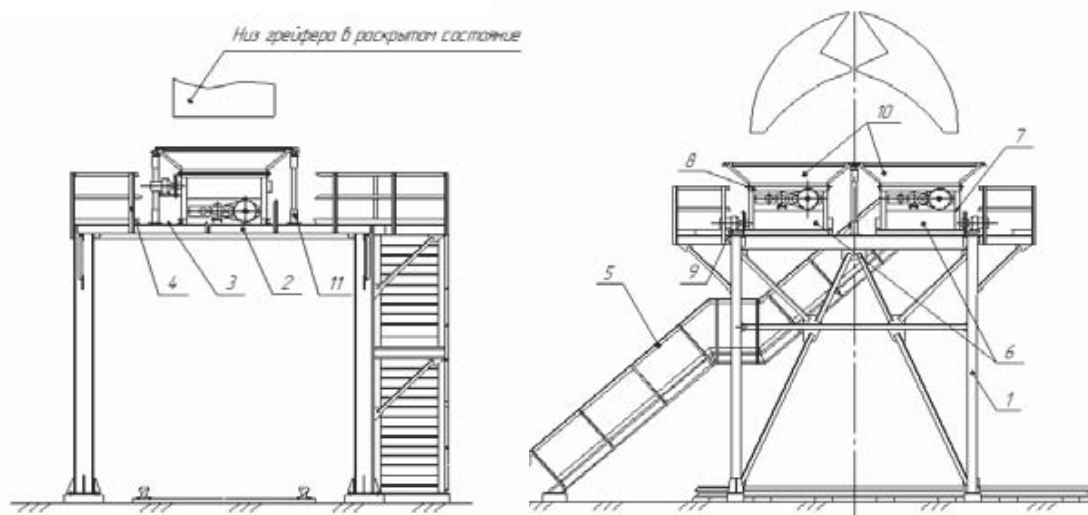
Конструкция гомогенизатора: 1 - стойка; 2 - портал; 3 - настил; 4-сварные ограждения; 5-лестница; 6-царга; 7-рама; 8-бункерная рама; 9-кронштейн; 10-бункер; 11-стойка
